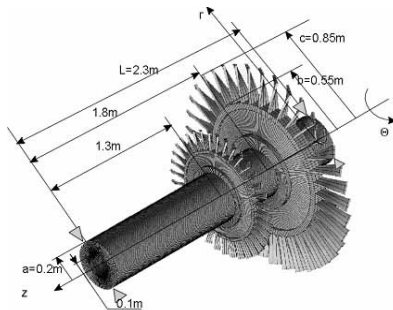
Трехмерная модель ротора с рабочими колесами.
